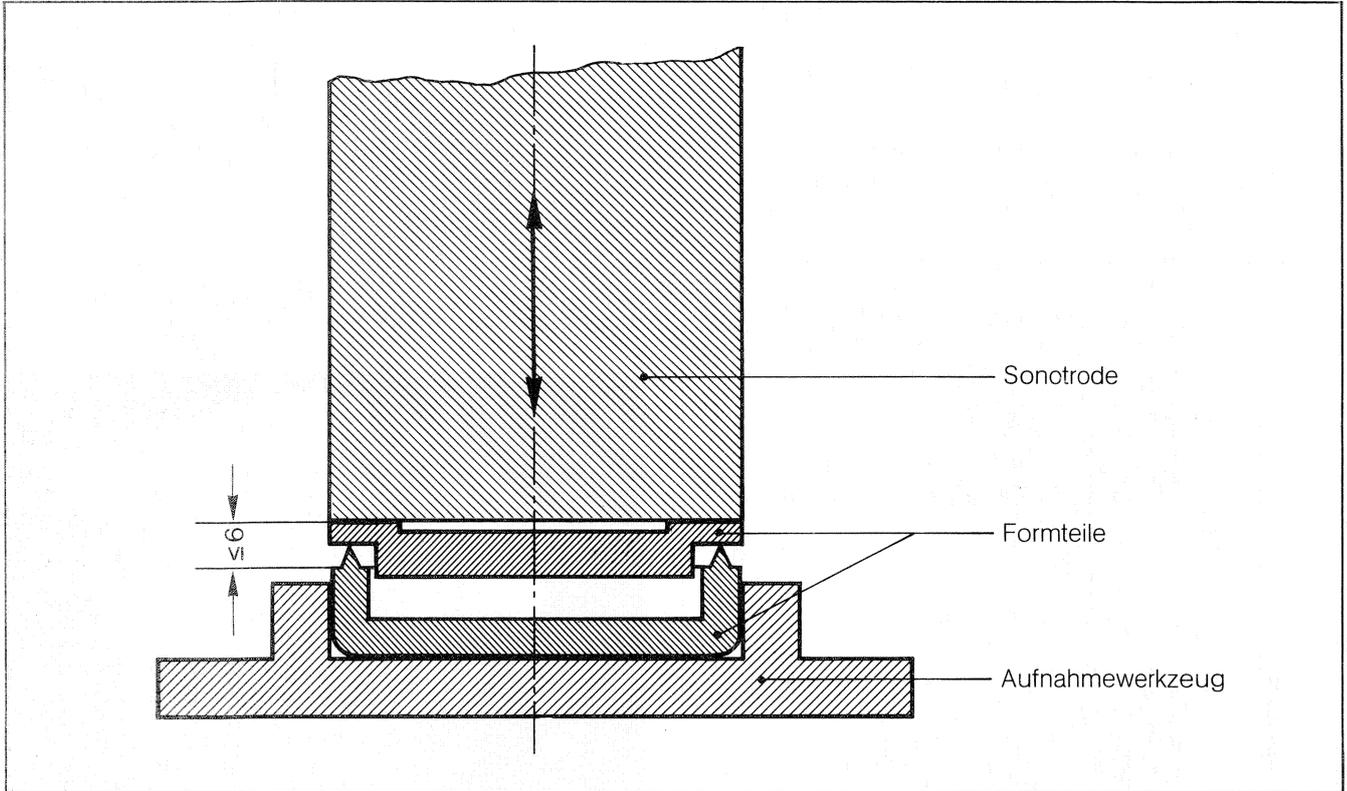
Ultraschallschweißen im Nahfeld
